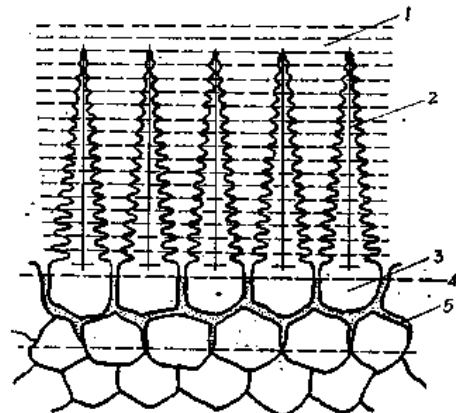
焊缝金属结晶凝固时熔合区状态示意图
